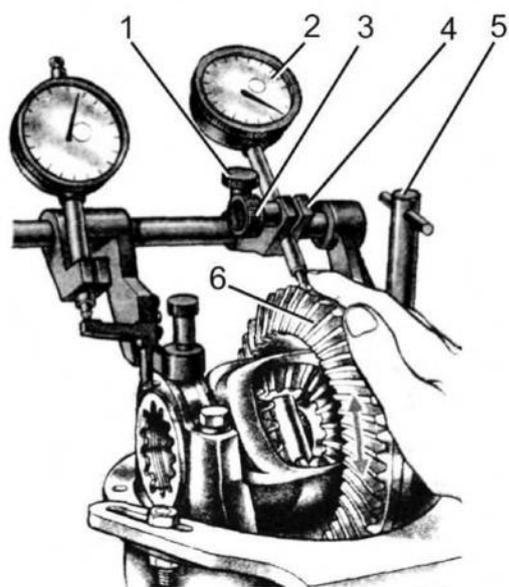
Проверка бокового зазора в зацеплении шестерен главной передачи приспособлением: 1 - винт затягивания кронштейна; 2 - индикатор для проверки бокового зазора в зацеплении ведущей и ведомой шестерен; 3 - винт крепления стержня индикатора; 4 - кронштейн индикатора; 5 - винт крепления; 6 - ведомая шестерня
